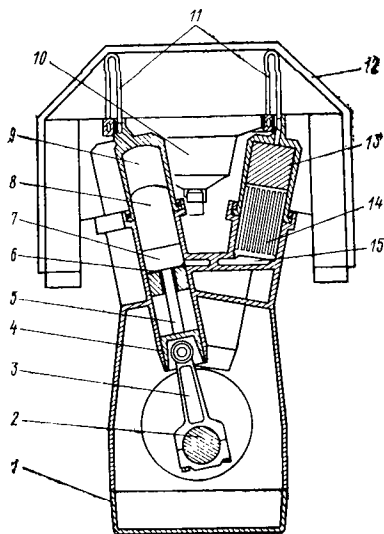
Конструктивная схема V-образного двигателя с кресткопфным механизмом двойного действия.
